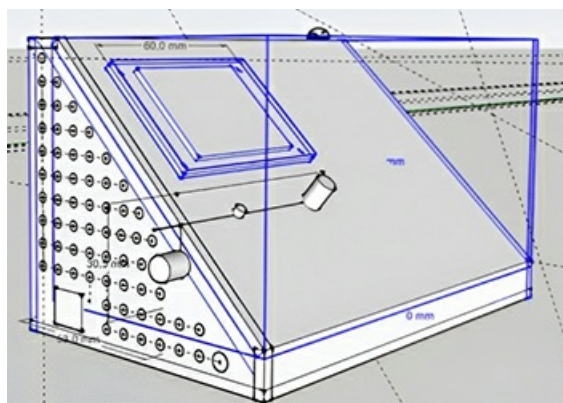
Внешний вид корпуса устройства, нарисованный в программе SketchUp
